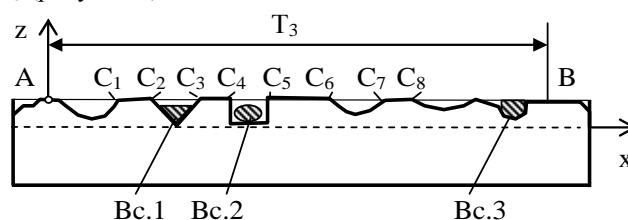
Заготовка з поперечними неровностями різного виду
